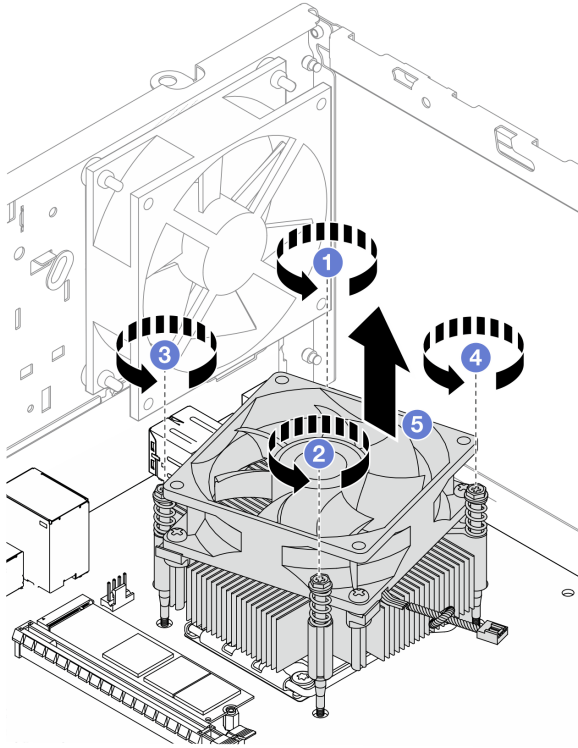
Entfernen des Kühlkörpers und Lüftermoduls
